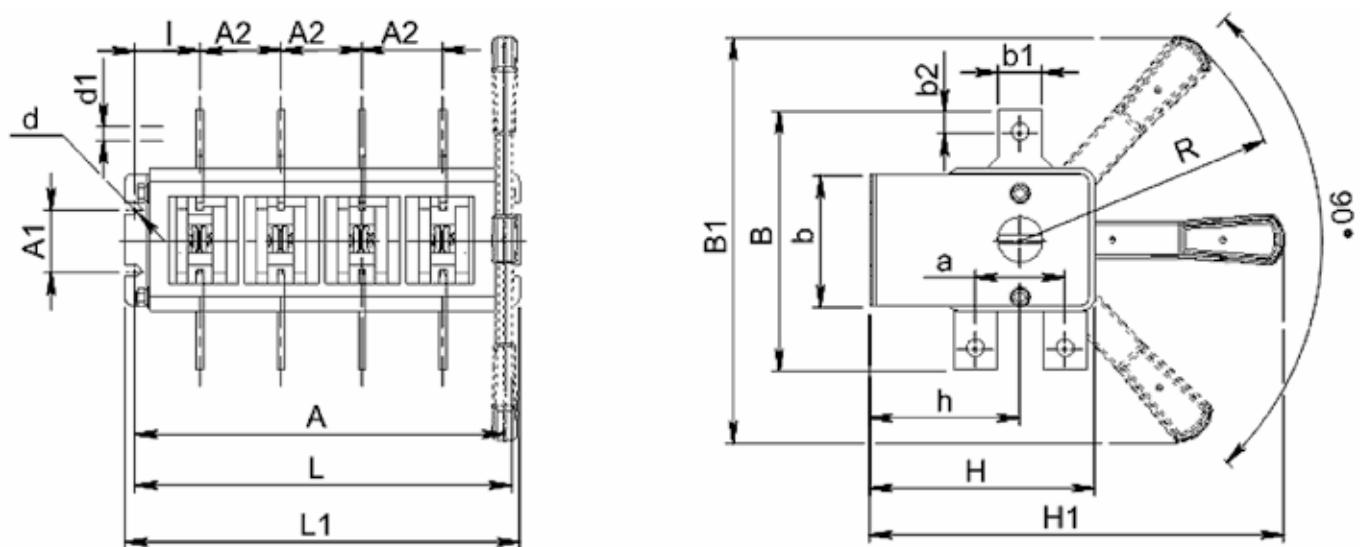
Выключатель-разъединитель на два направления 4-полюсный с боковой рукояткой
